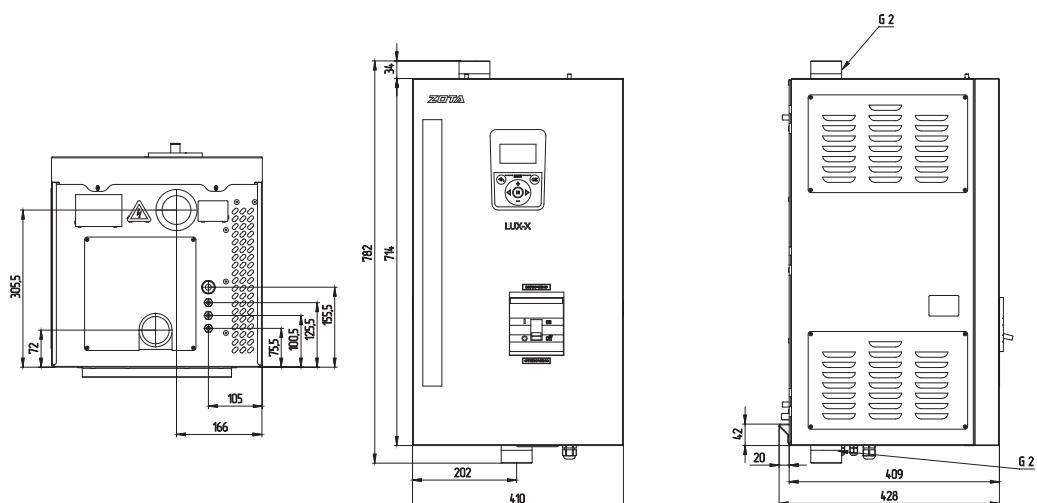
Габаритные размеры ZOTA LUX-X 60-100
